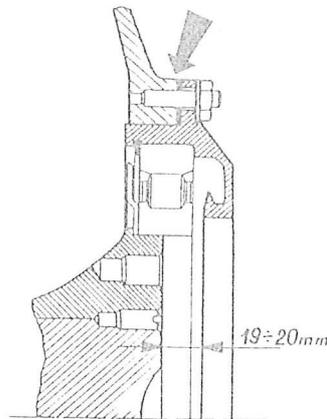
Lage der Öffnung für den Ölüberlauf beim Anbau des Lagerdeckels
